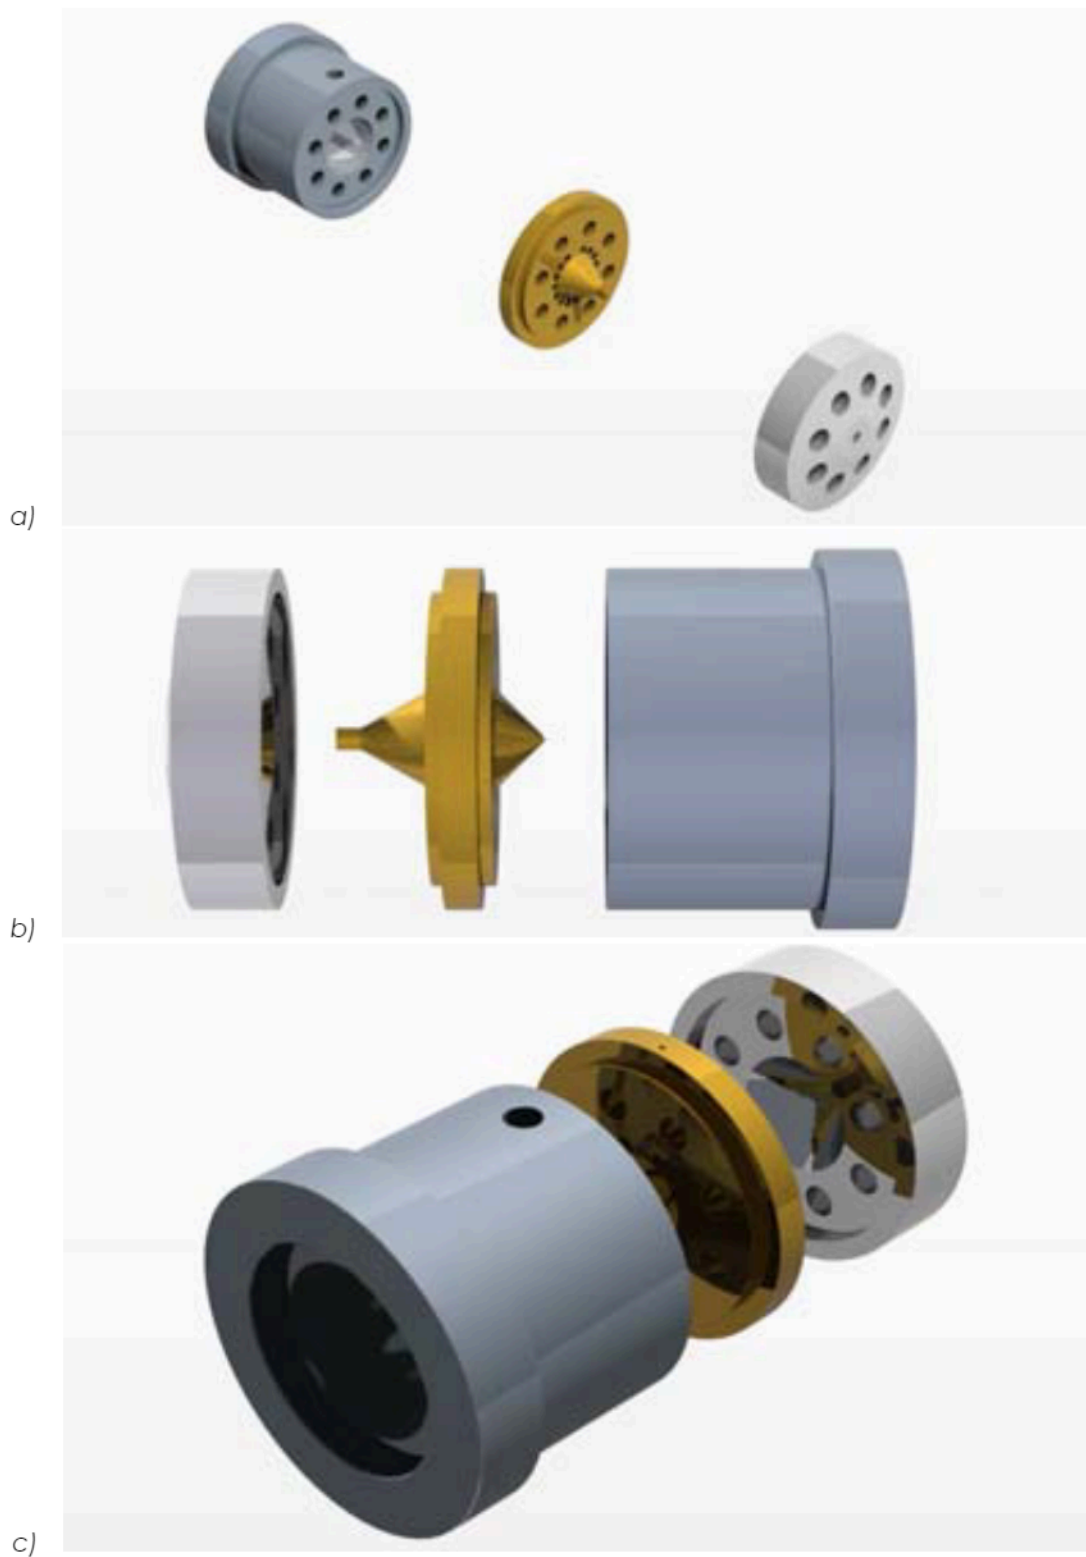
a), b), c) son imágenes en explosivo de los componentes del dado (soporte, mandril y boquilla) en su posición de ensamble.
